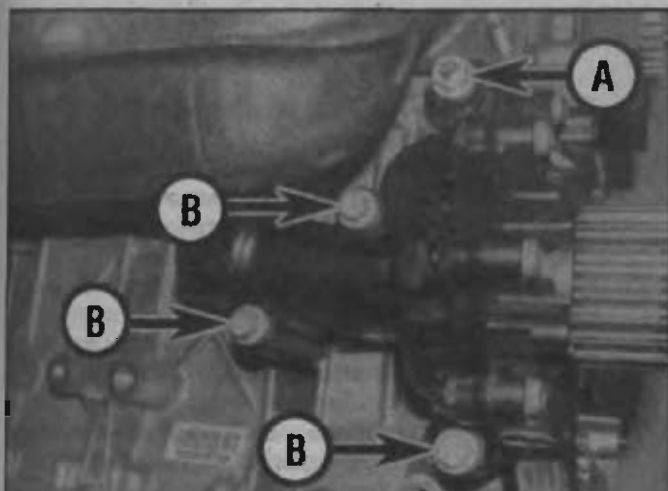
Расположение гайки (А) и болтов (В) крепления водяного насоса к задней части блока цилиндров двигателя 1,8 л
